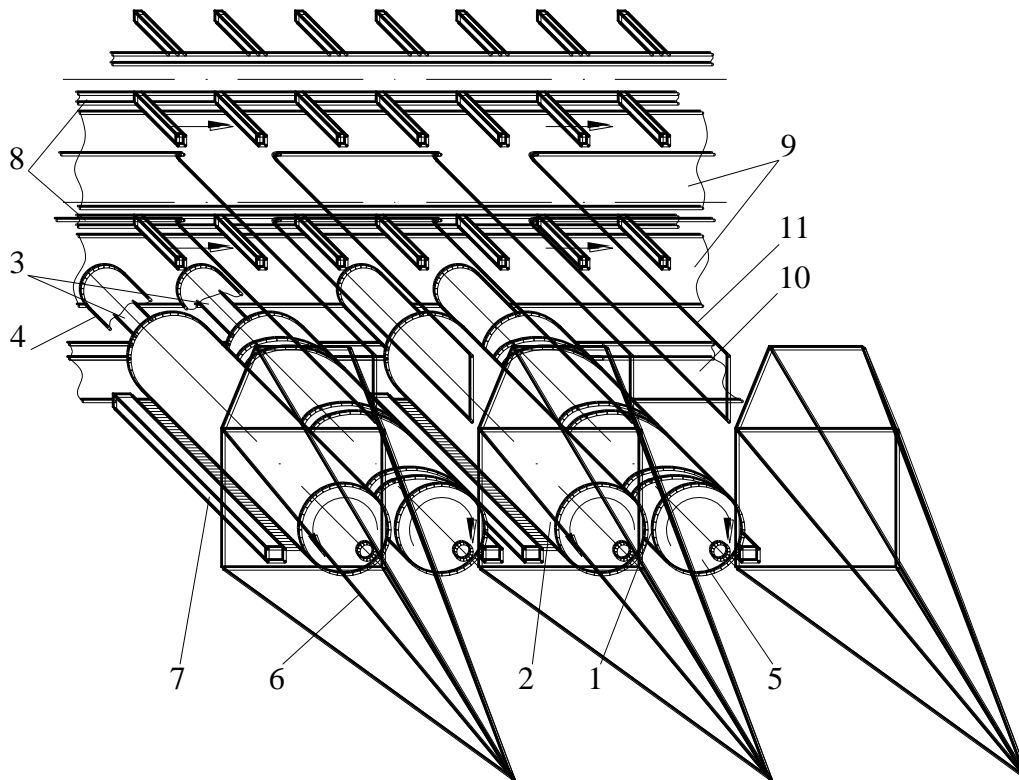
Roller flax puller / Вальцьовий бральний апарат
